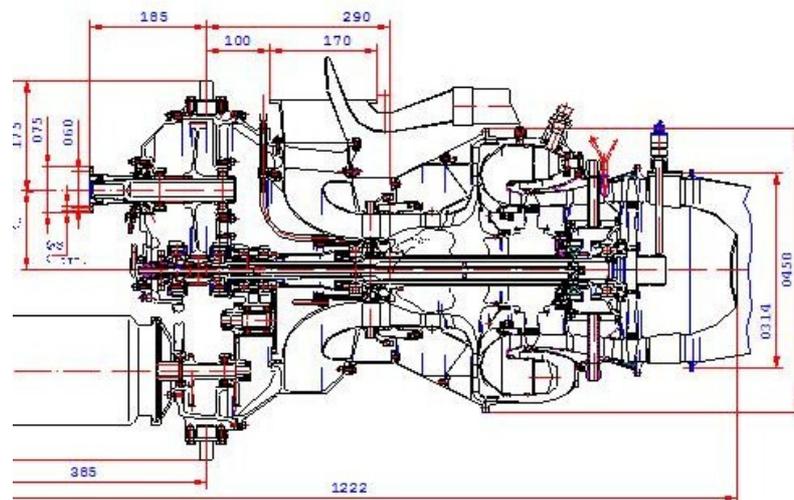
Конструктивная схема двигателя НК-123BP-B
